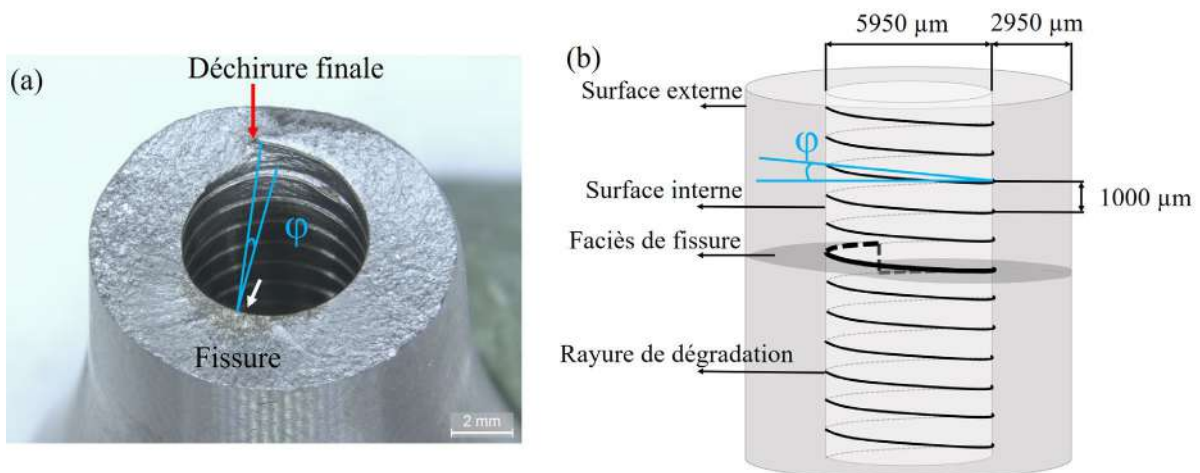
Schéma pour illustrer le plan de fissuration pour l'état de surface dégradé.
